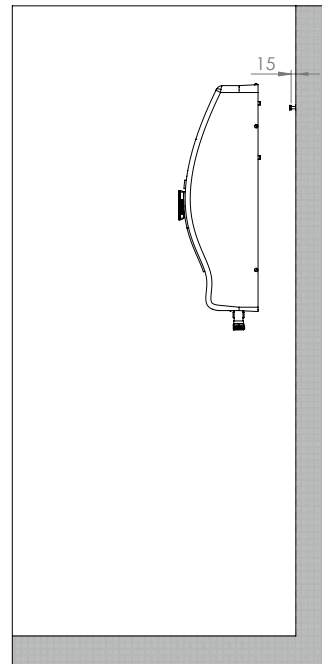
Befestigungsschrauben - versetzt zur Wand
